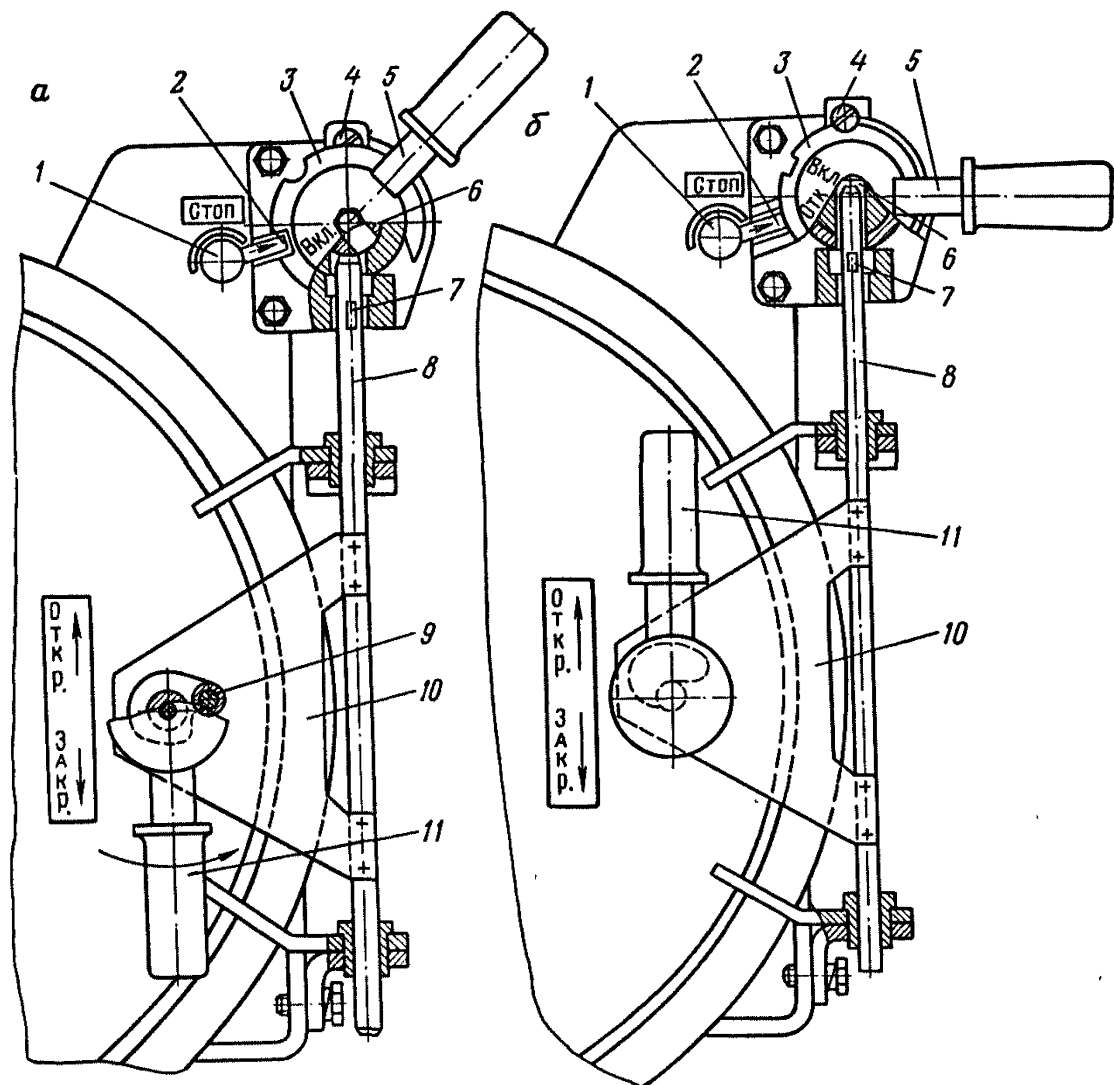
Блокировка разъединителя с быстрооткрываемой крышкой и кнопкой «Стоп» станций СУВ-1Л-100 и СУВ-2Л-120:
